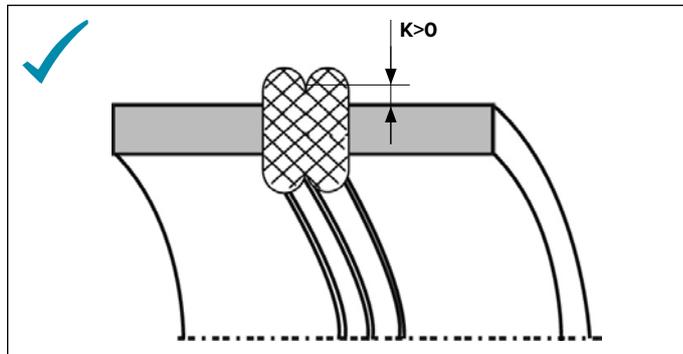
Vue en coupe d'une bonne ligne de soudure.
